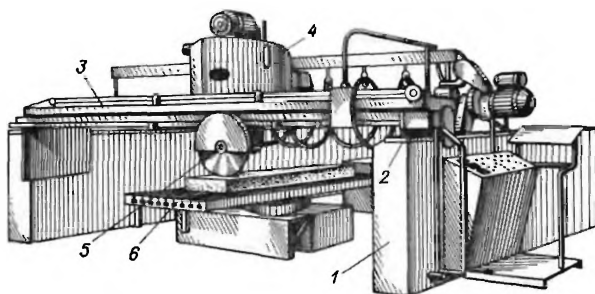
Фрезерно-окантовочный мостовой станок модели «Торпедо-310» фирмы «Карл Майер»
